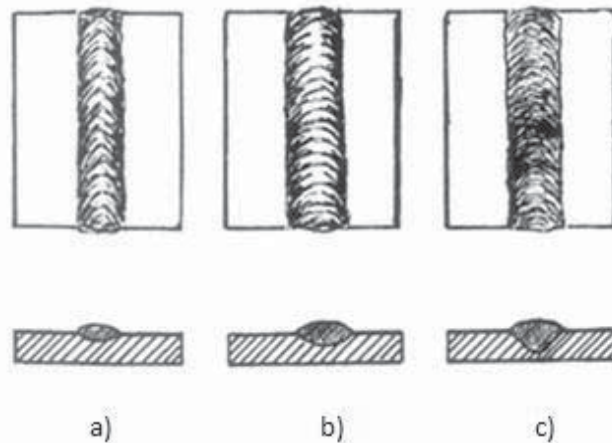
Efecto del voltaje en el tamaño y forma del cordón de soldadura: a) 21 volts, b) 24 volts y c) 27 volts
